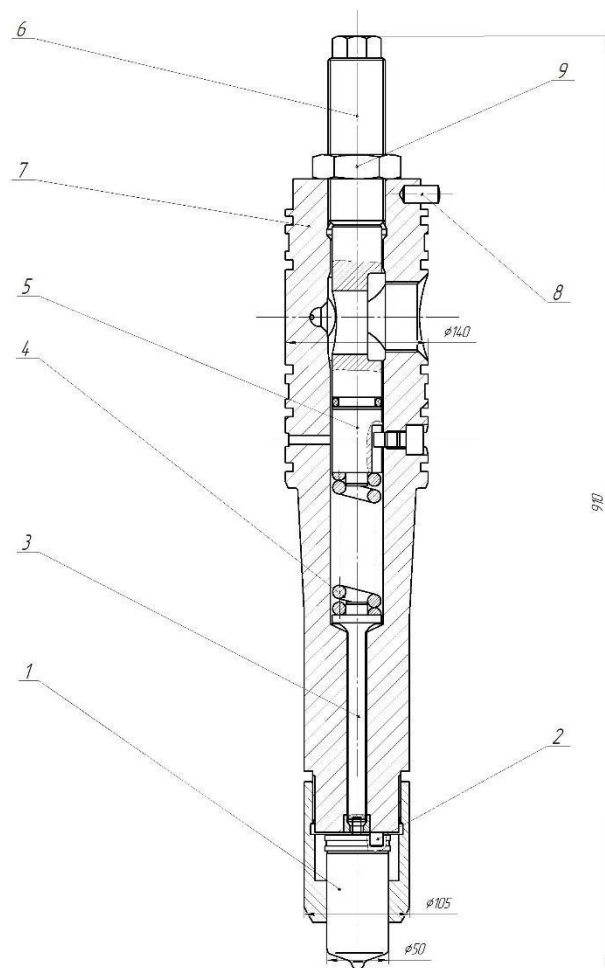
Форсунка середньообертового суднового двигуна МАК 12M43C [37-40]: 1 – корпус розпилювача; 2 – штифт установочний; 3 – штанга приводу голчастого клапана; 4 – навантажуюча пружина; 5 – упор навантажуючої пружини; 6 – гвинт навантажуючої пружини; 7 – гвинт регулювання попереднього затягування навантажуючої пружини; 8 – установочний штифт; 9 – стопорна гайка
